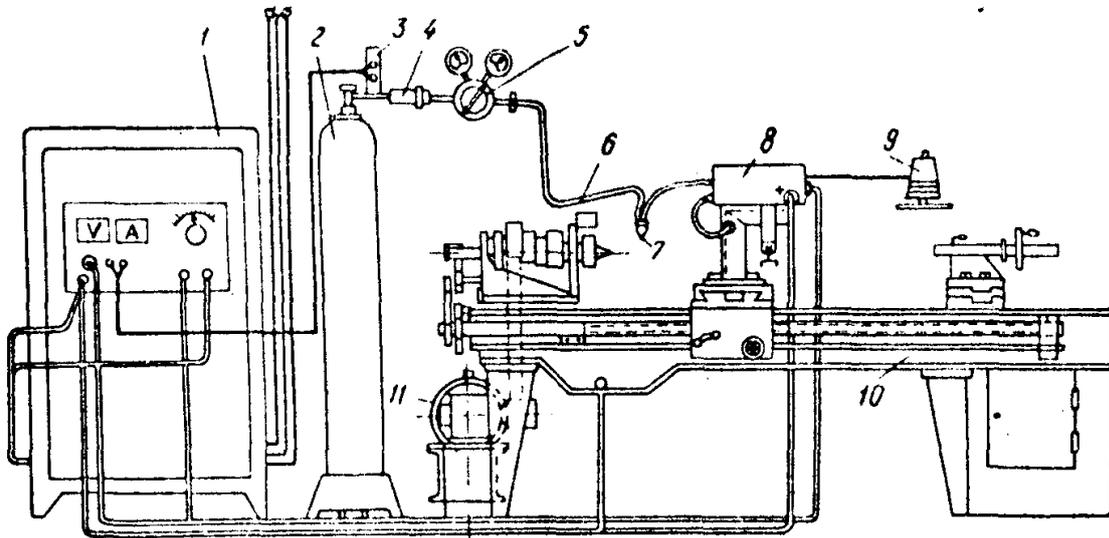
Автоматическая установка для наплавки деталей с среде углекислого газа: 1- селеновый выпрямитель типа ВС-200; 2- баллон с углекислотой; 3-электроподогреватель газа; 4- осушитель углекислого газа; 5- редуктор; 6-резиновый шланг для подачи газа к горелке; 7-горелка с мундштуком; 8-механизм для подачи сварочной проволоки к месту сварки; 9-турникет с проволокой; 10-токарно-винторезный станок; 11-электродвигатель; А-амперметр; V-вольтметр
